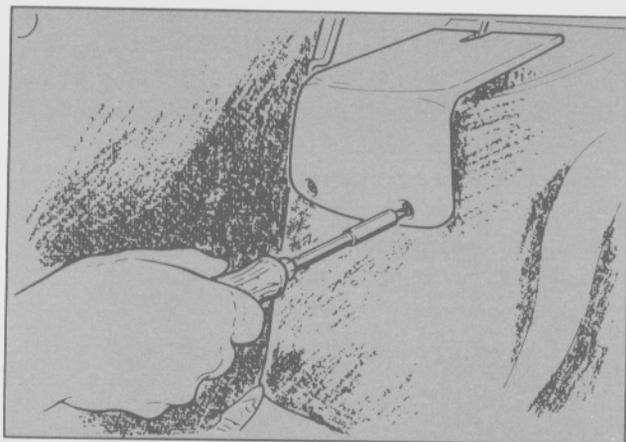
Tapa de acceso al montaje superior del amortiguador (GHIA)
